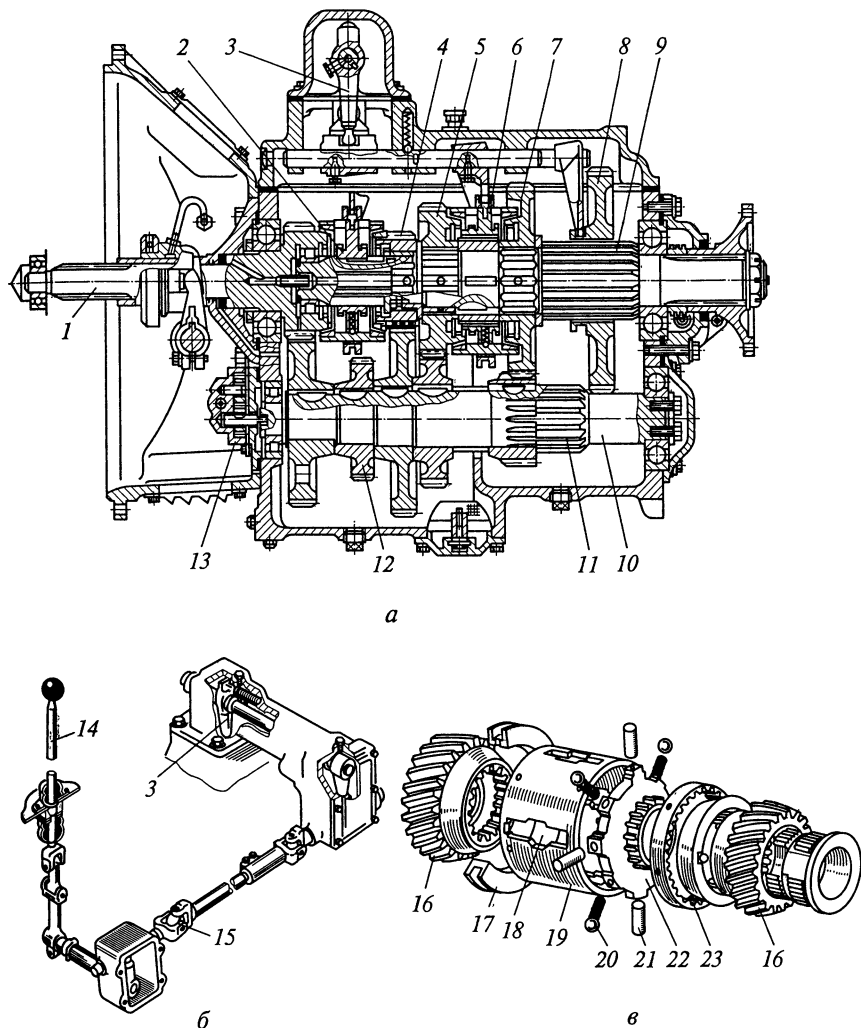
Коробка передач грузовых автомобилей МАЗ:
